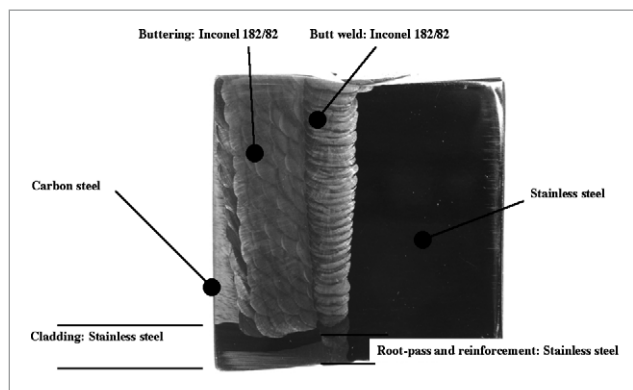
Soldaduras de unión de Inconel 182/82, revestido con acero inoxidable.
